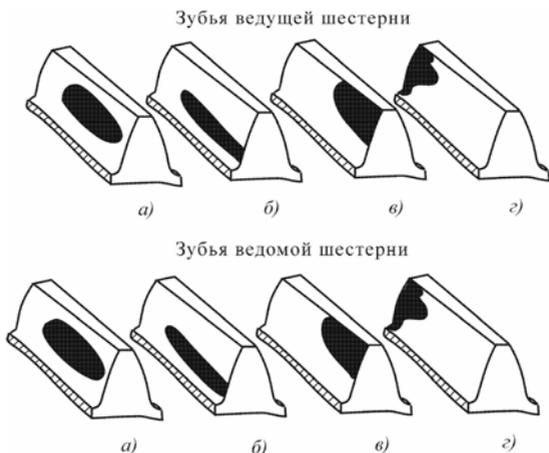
Проверка при регулировке зацепления зубьев конической зубчатой передачи с помощью краски:
